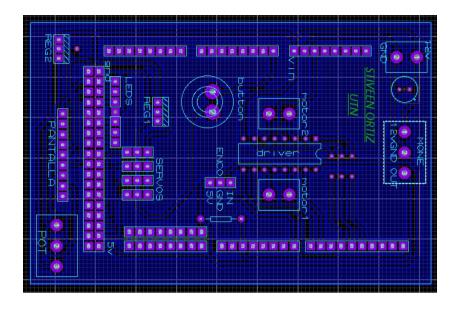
Diseño de shield para Arduino Fuente: Autor.
